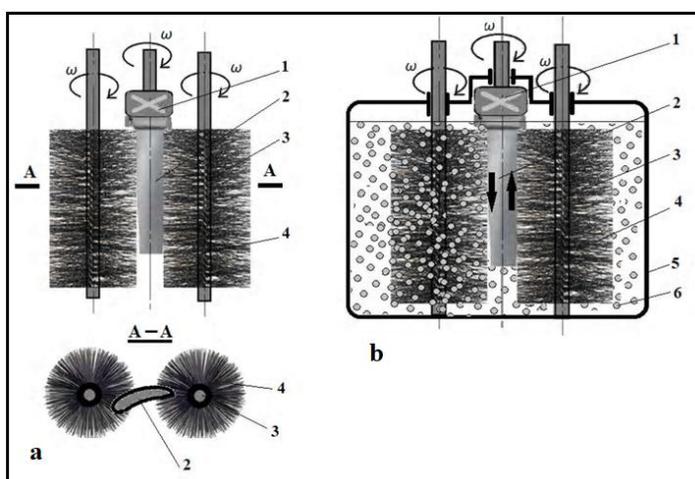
Способ полирования лопаток ГТД методом СЭПГЩ [5]. (1 – держатель; 2 – обрабатываемая деталь; 3 – металлический стержень-электрод щетки; 4 – щетка; 5 – рабочий контейнер; 6 – гранулы, пропитанные электролитом)
